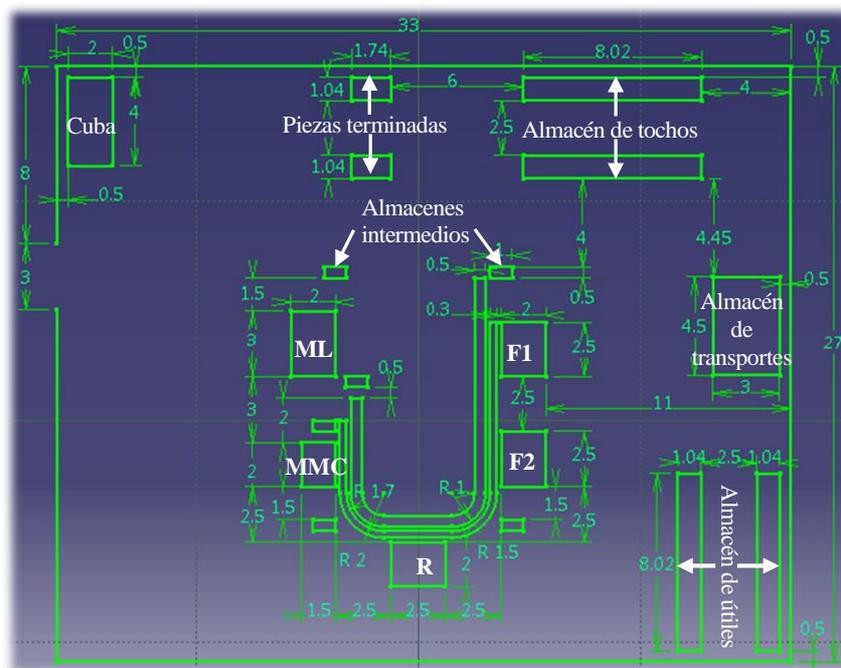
26. Nuevo layout de la planta de fabricación propuesta en la alternativa 3. F1, fresadora 1; R, rectificadora; MMC, máquina de medición de coordenadas; ML, máquina de limpieza. Fuente: Elaboración propia.
